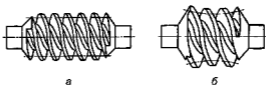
Виды червяков: *а* – цилиндрический; *б* – глобоидный
